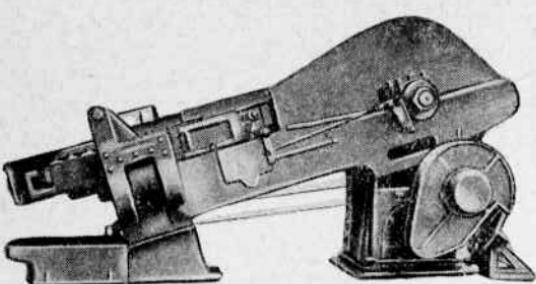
Резьбонакатный полуавтомат фирмы Кайзер для накатывания резьбы на обоих концах шпильки.
